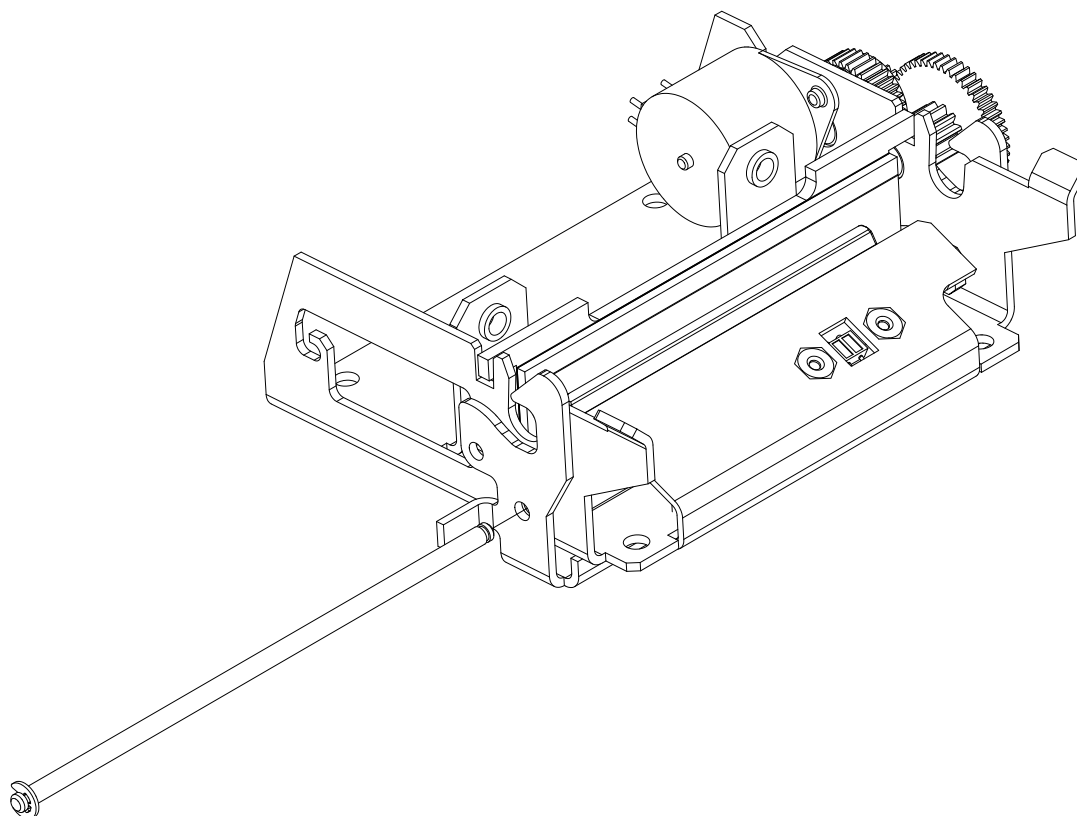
Ось защелки прижимного вала чековой ленты.
